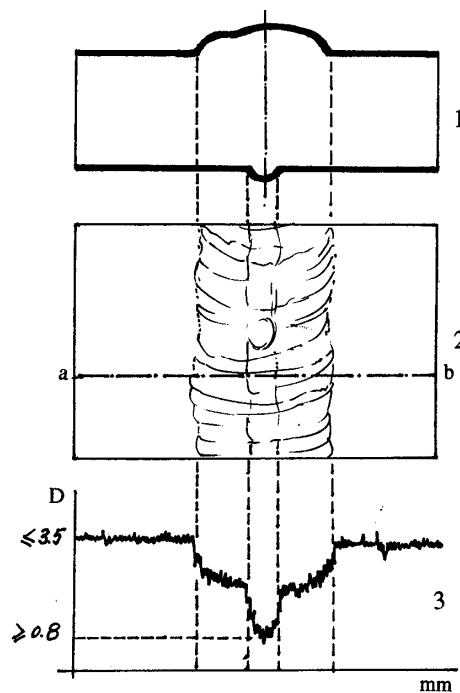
Interpretación radiográfica básica de la imagen de un cordón de soldadura en "V" simétrica.
